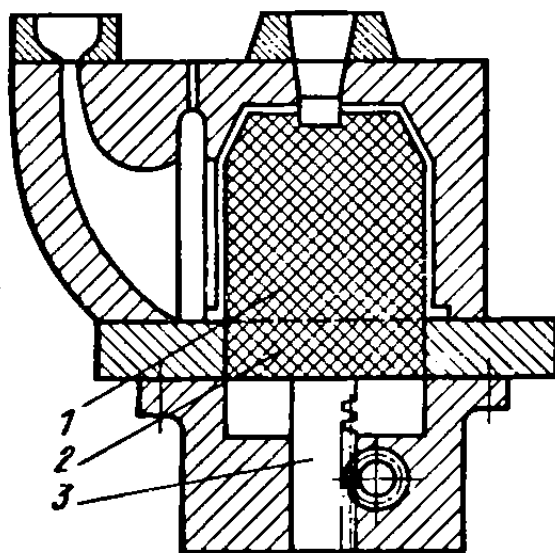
Кокиль с реечным механизмом перемещения металлического стержня
